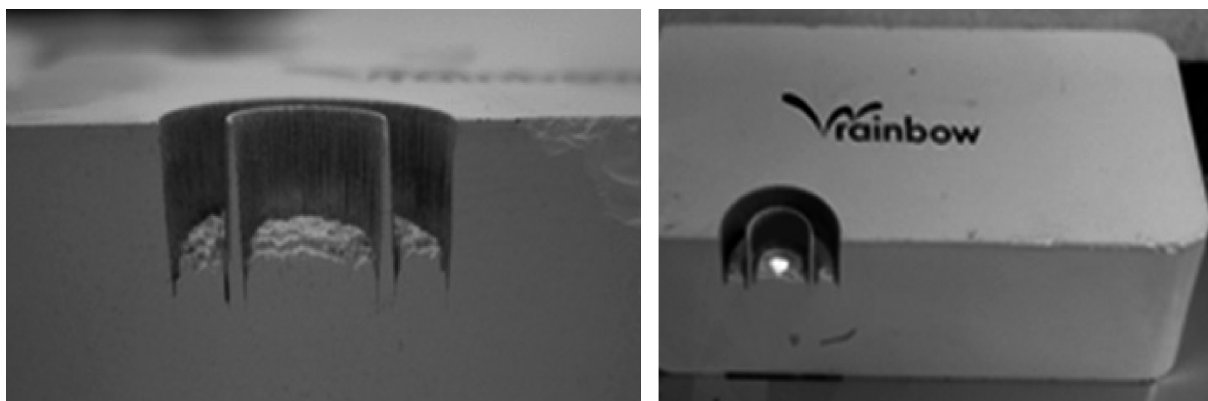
Половинный разрез цилиндрической конструкции с толщиной стенки 50 мкм (вид сбоку и сверху).
